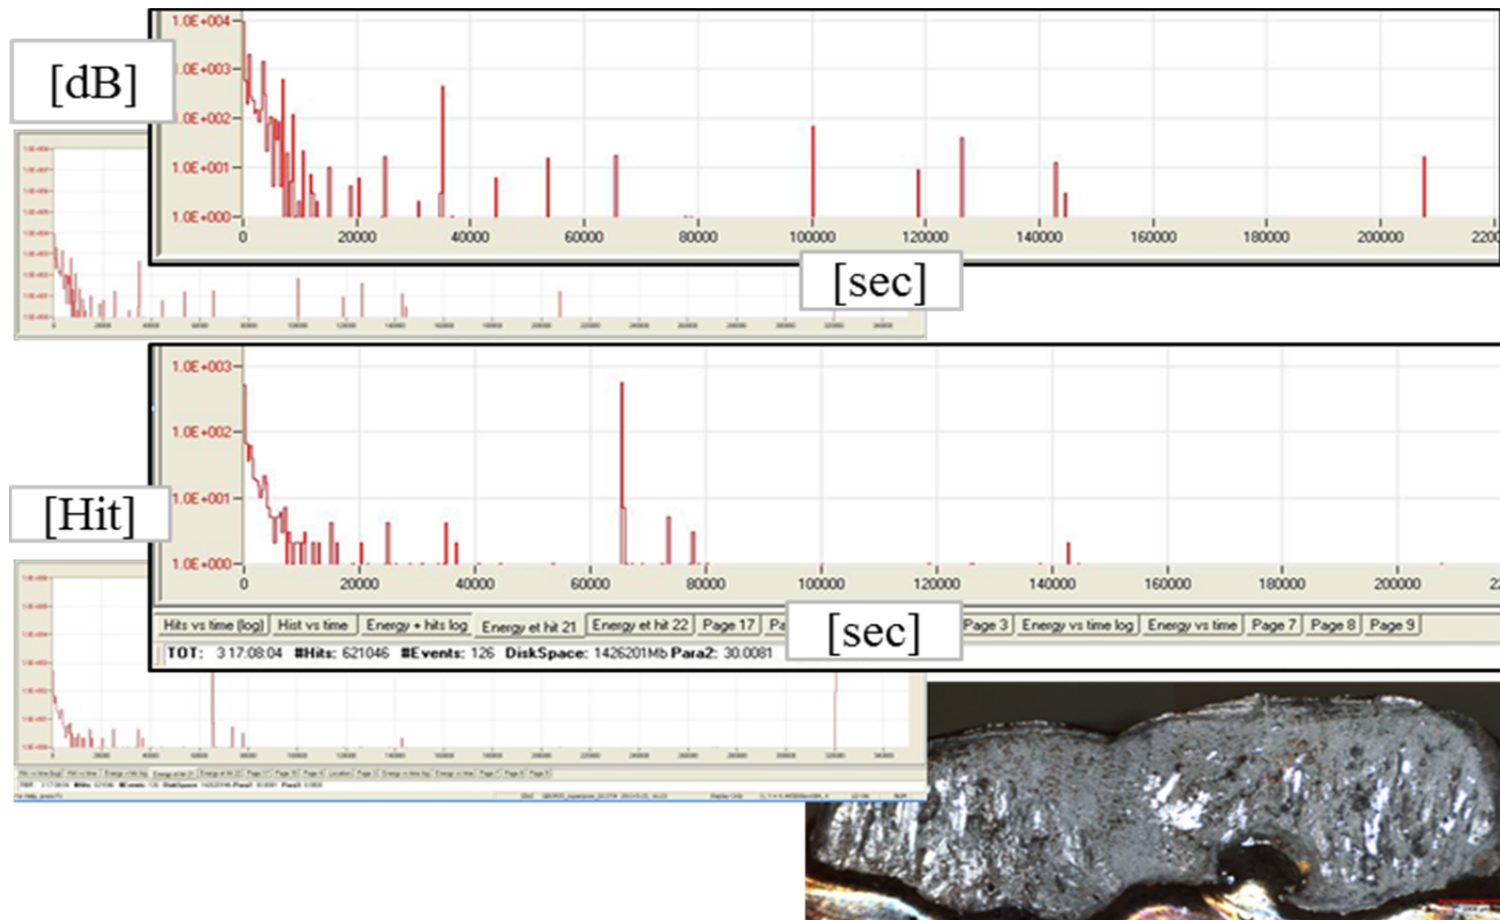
Résultat d'un essai d'émission acoustique sur une éprouvette GBOP et surfaces de rupture de cette même éprouvette. Soudure faite sans préchauffage et avec montage de refroidissement
